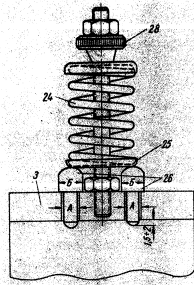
Узел регулировки тока отпуска; значение шпирт приведено под рис. 2.
